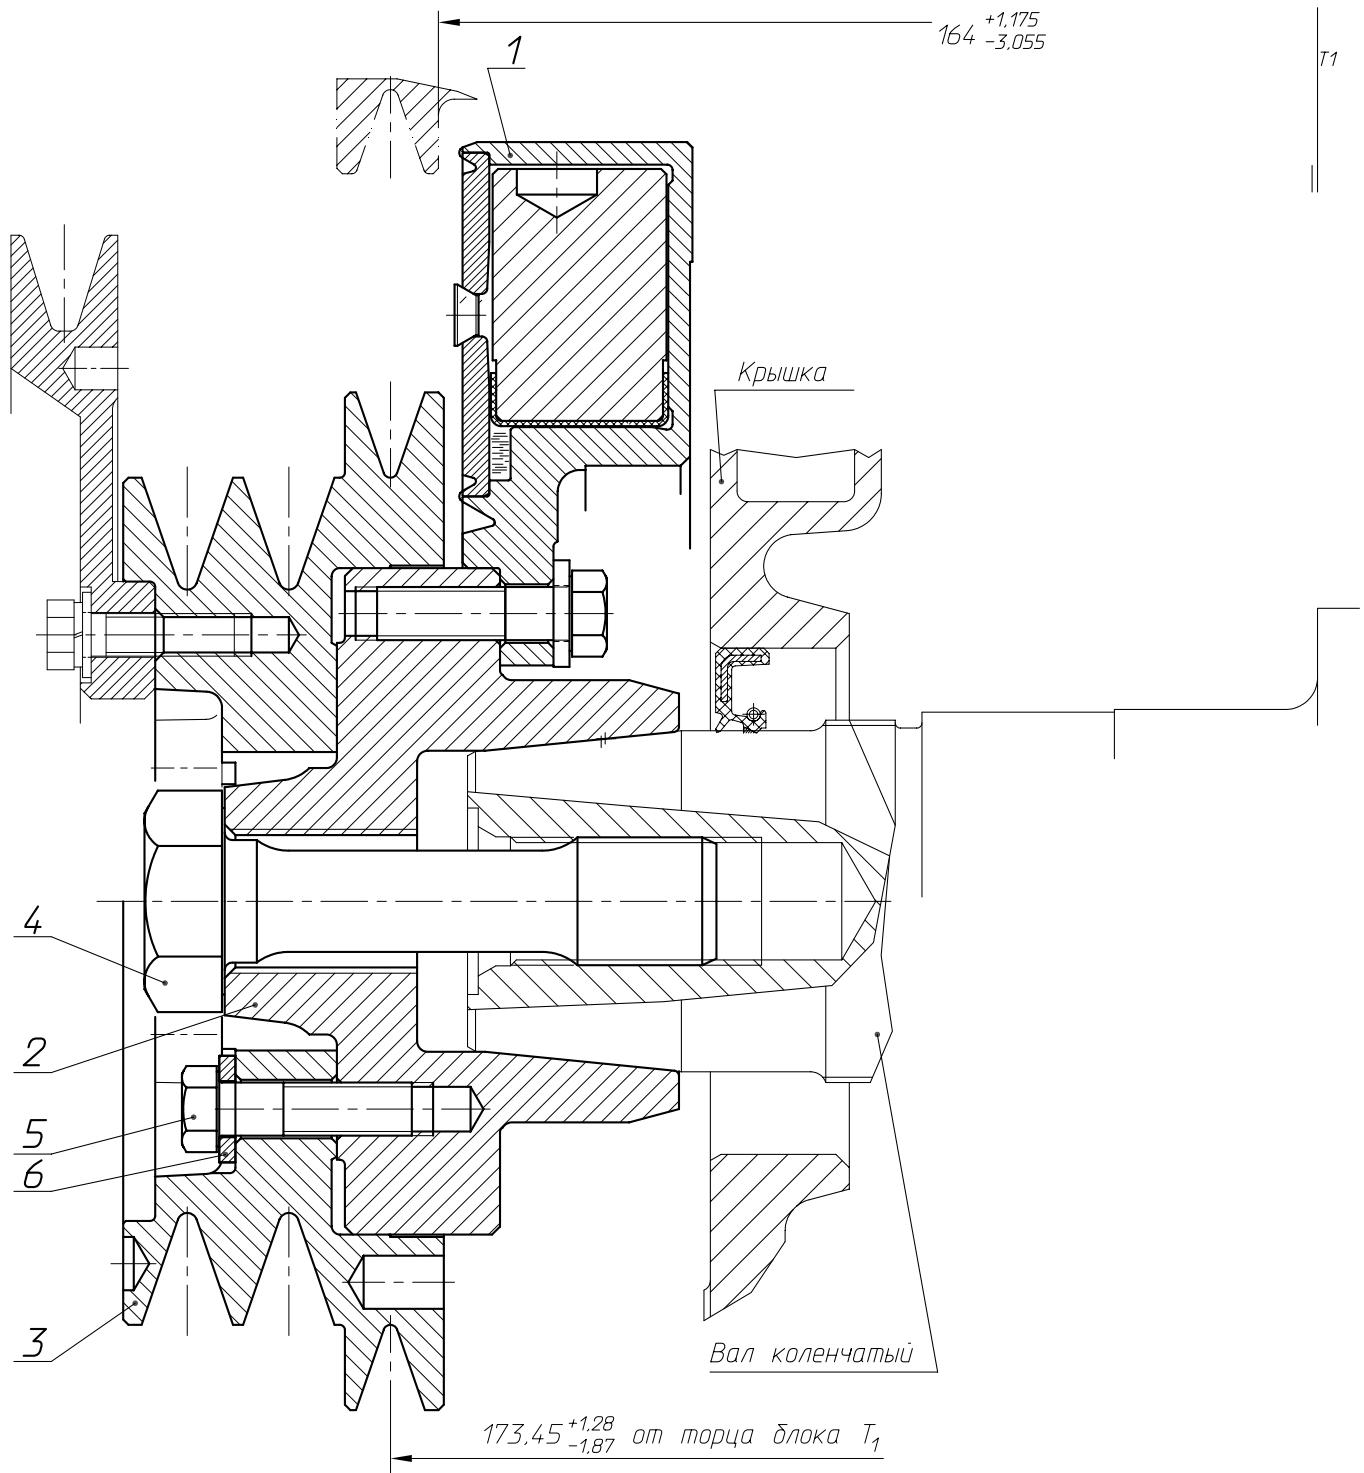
Установка гасителя и шкива на двигатель, 7511.1005050
